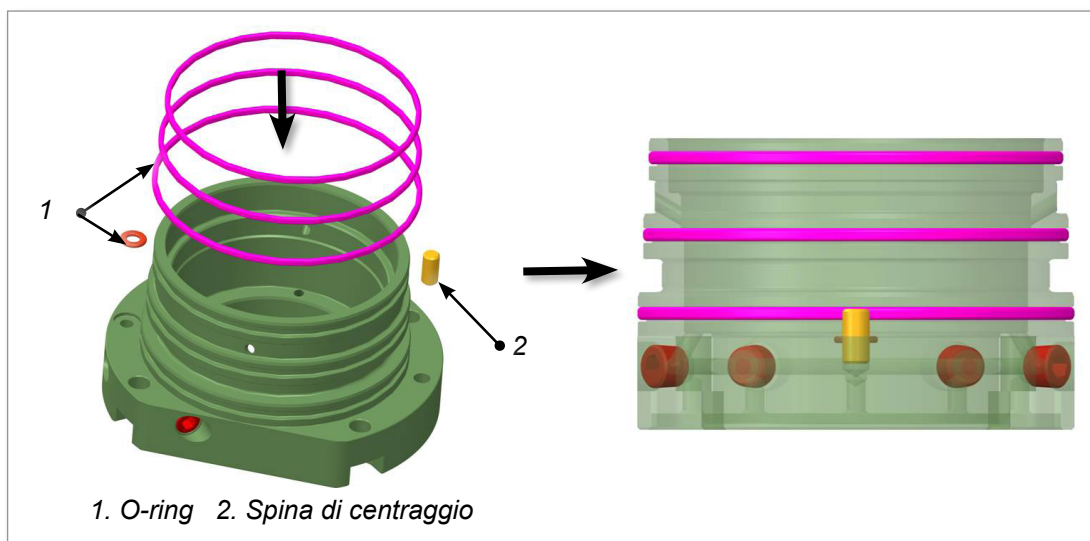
Installazione degli O-ring e della spina di centraggio
